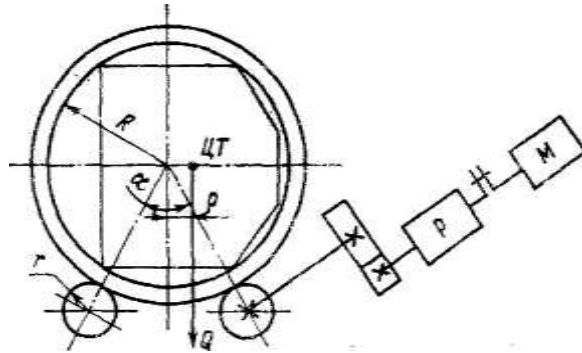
Расчетная схема роликового стенда с жесткой кинематической связью: M — электродвигатель; P — редуктор; $ЦТ$ — центр тяжести
